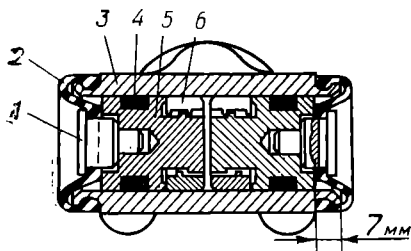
Колесный тормозной цилиндр с устройствами для автоматической регулировки зазоров между колодками и барабаном:
